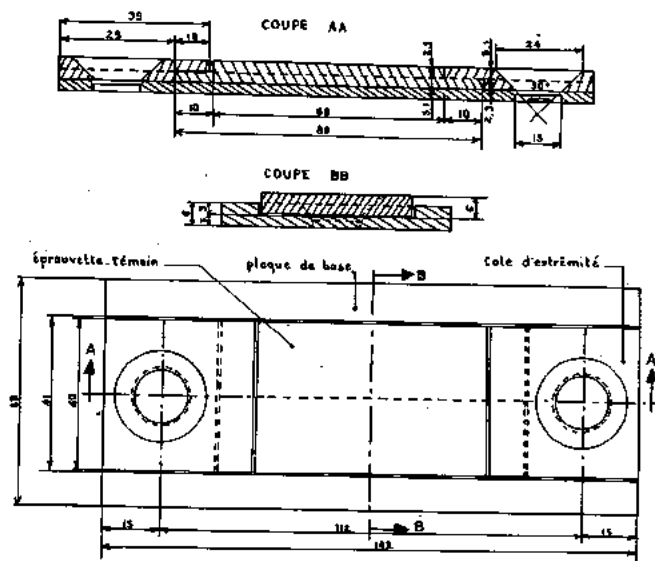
Epruvette-témoin pour la mesure de la corrosion.
